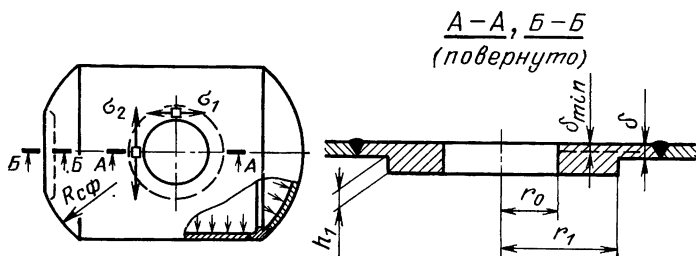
Конструктивный вид окантовки отверстия в оболочках емкости; действующие напряжения
